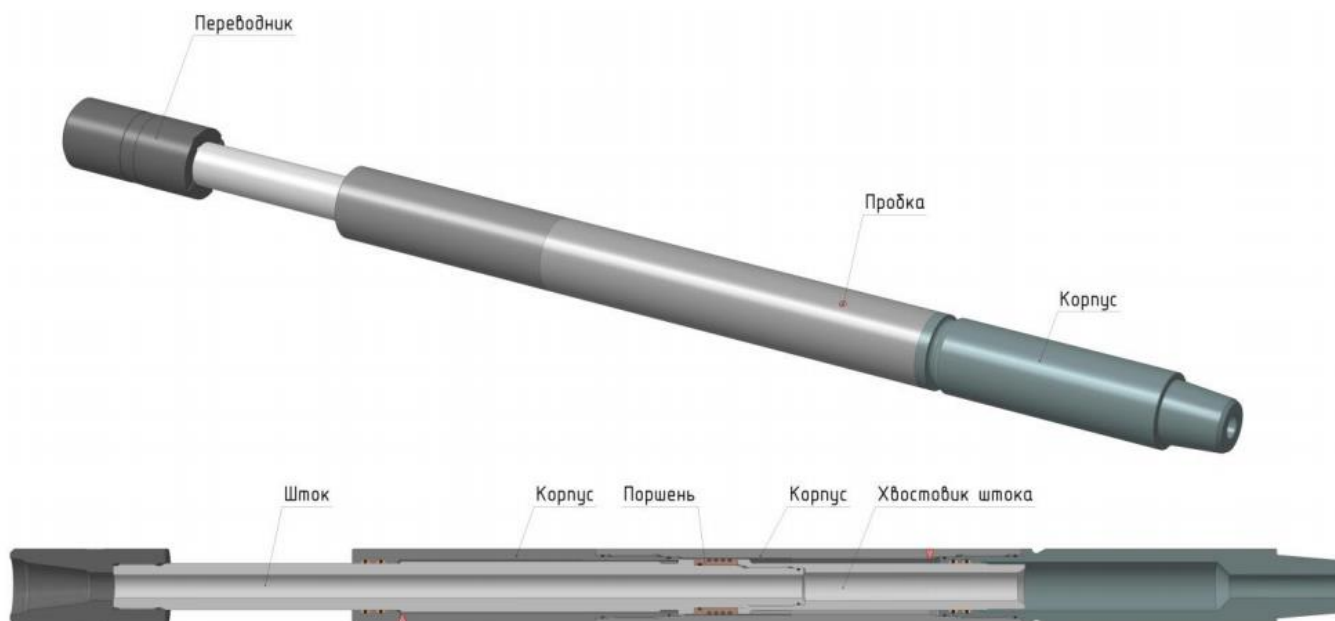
Ясс гидравлический конструкции БИТТЕХНИКА
